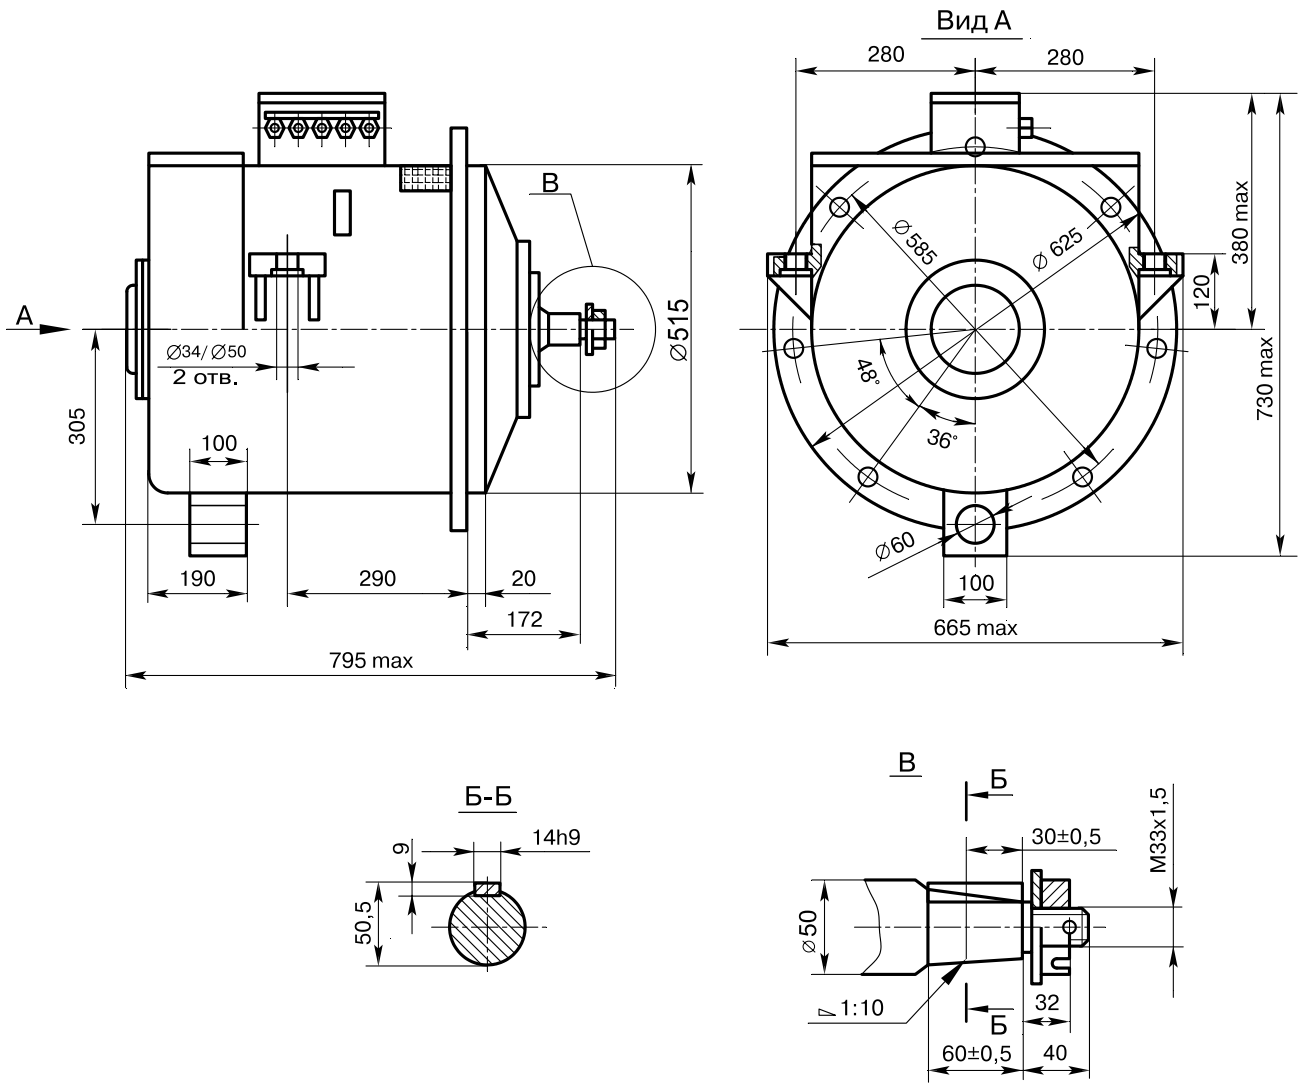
Габаритные и установочные размеры электродвигателя ДТН–45/27
